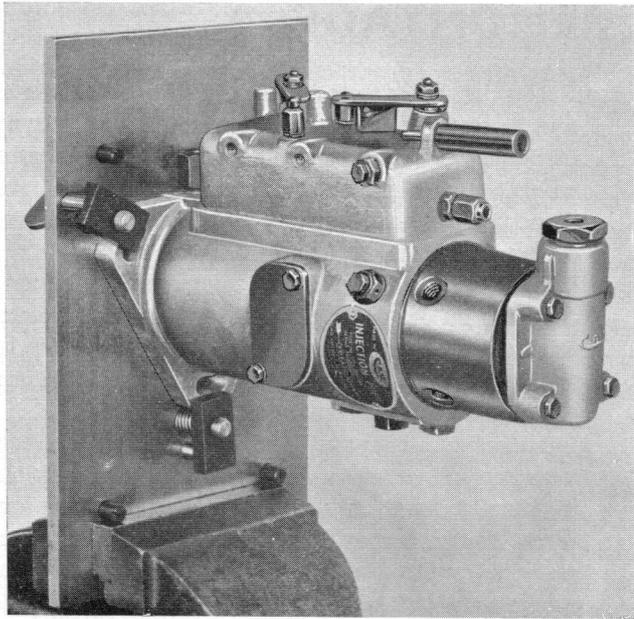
Pompe à régulateur mécanique montée sur plaque support de démontage et de remontage
